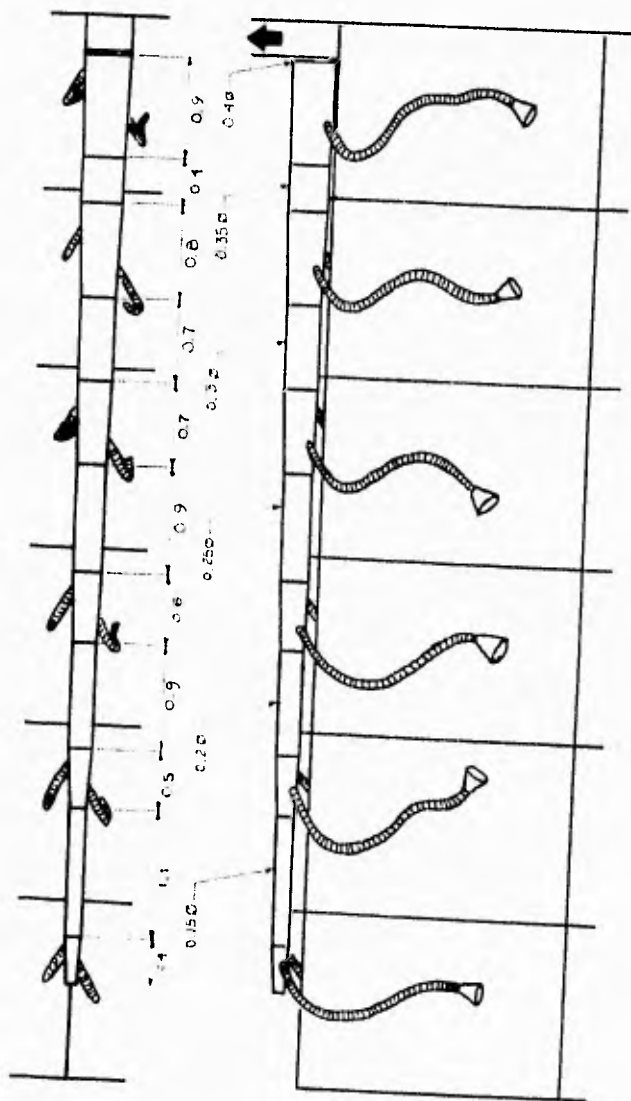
3o propuesta. Sistema de extracción para soldadura por arco
